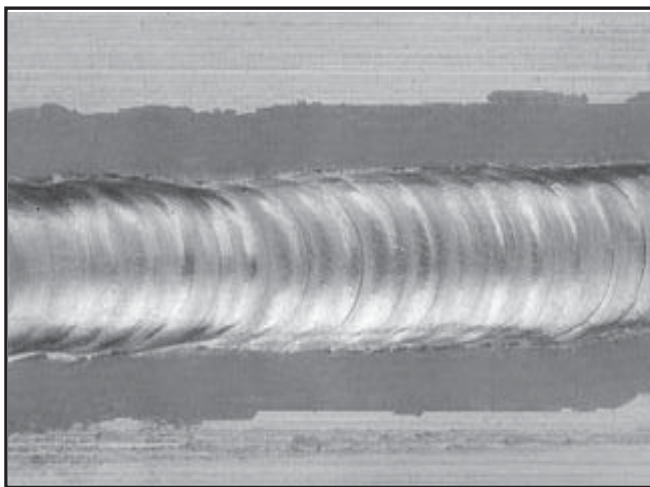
La calidad de cordones de soldadura de este proceso es muy buena.
